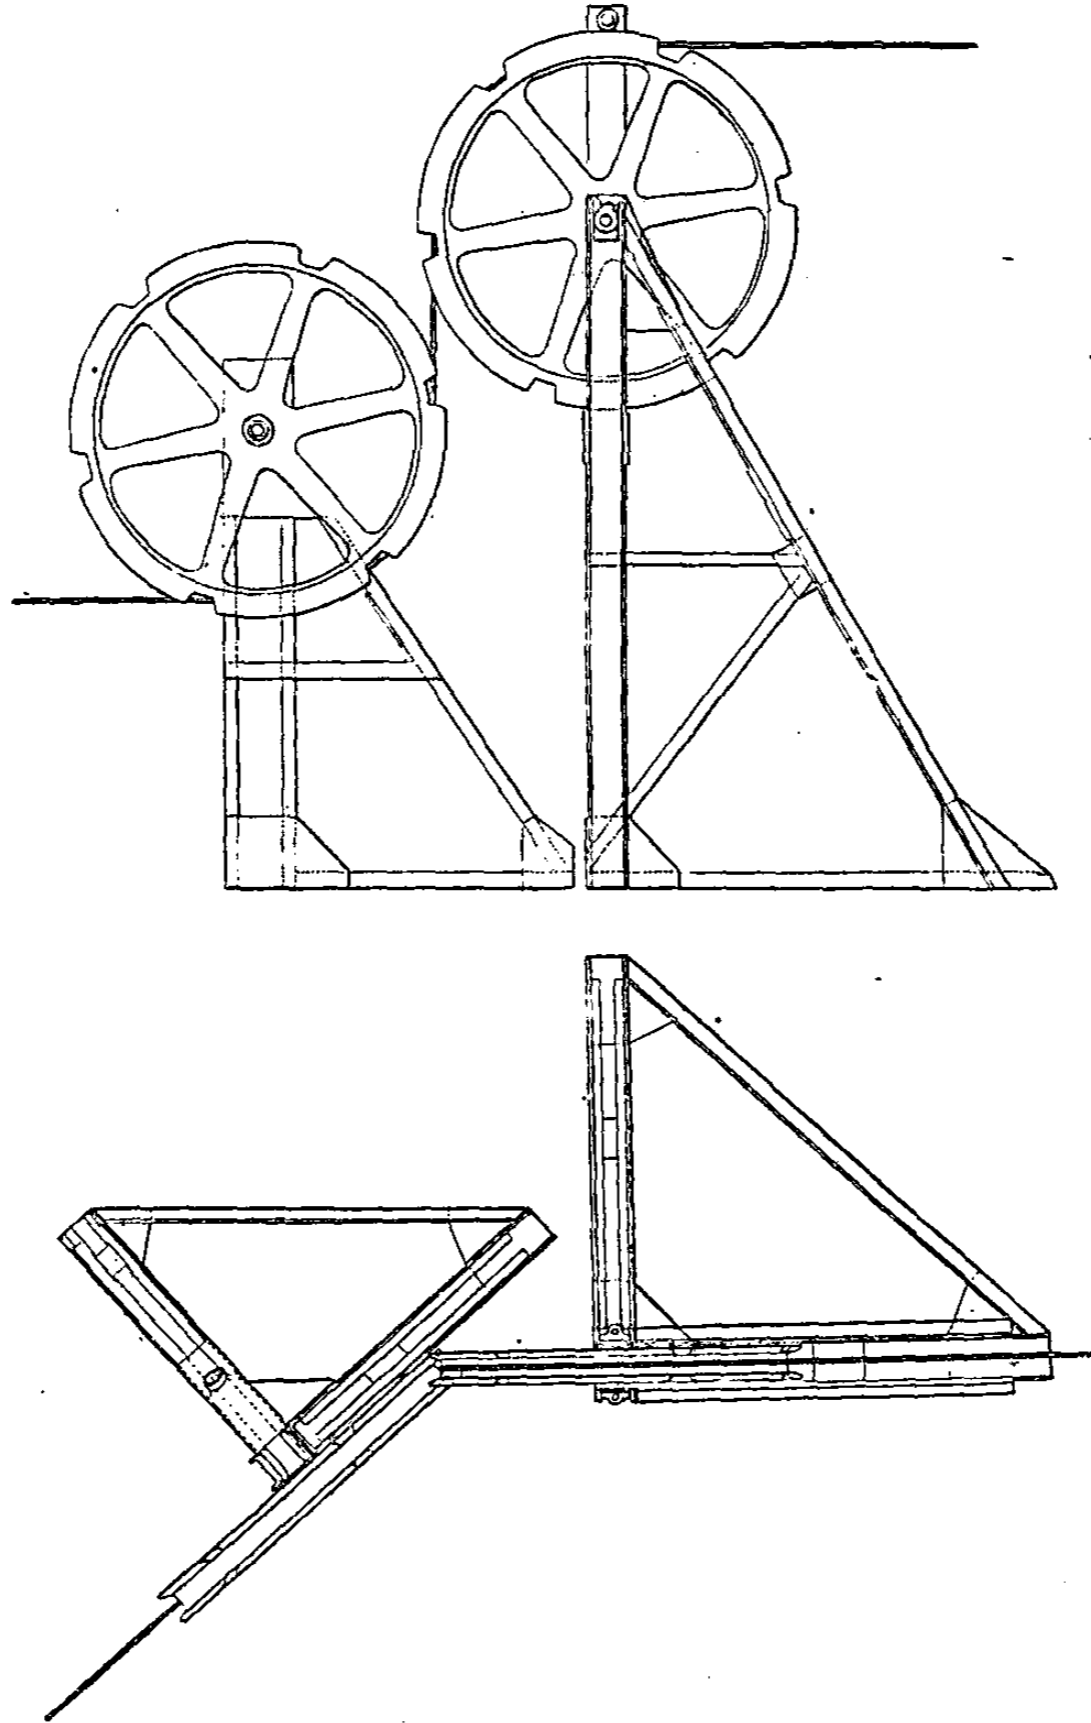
et 568. — *Élévation et plan d'une poulie double pour angle concave (dans l'élevation, la poulie inférieure est supposée rabattue dans le plan de la poulie supérieure).
